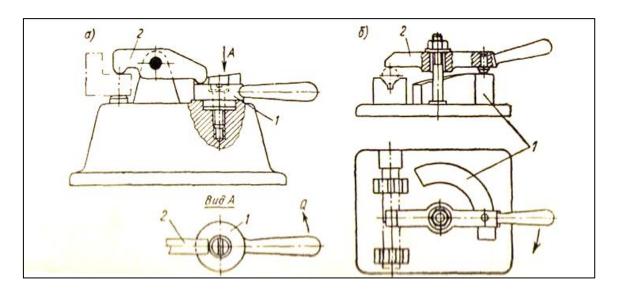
Торцовые кулачки: а – винтовой профиль кулачка; б – клиновой профиль кулачка
